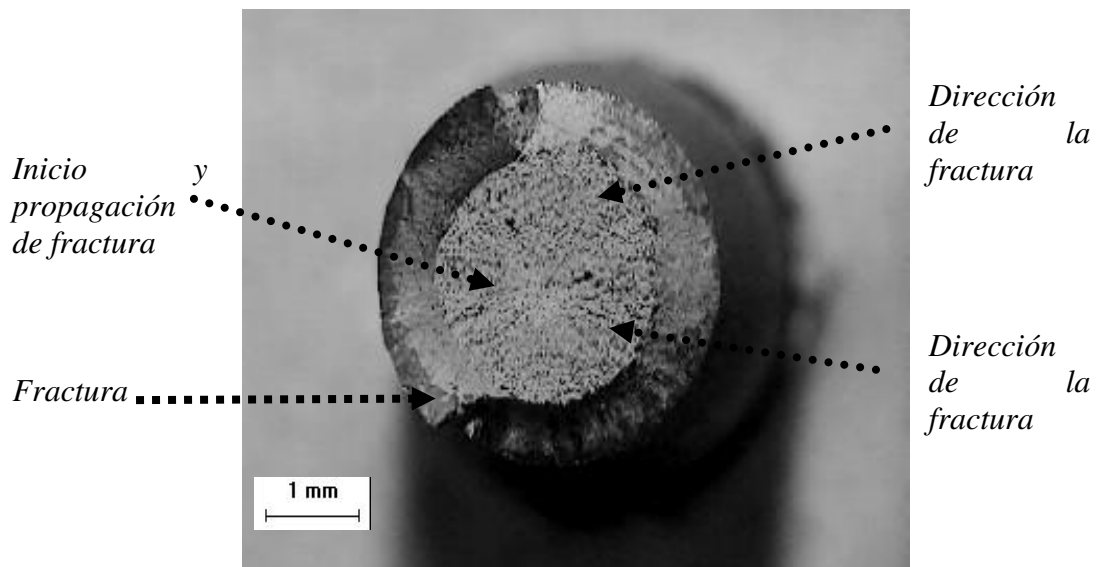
Macrografía de la probeta 12, tipo de fractura frágil
